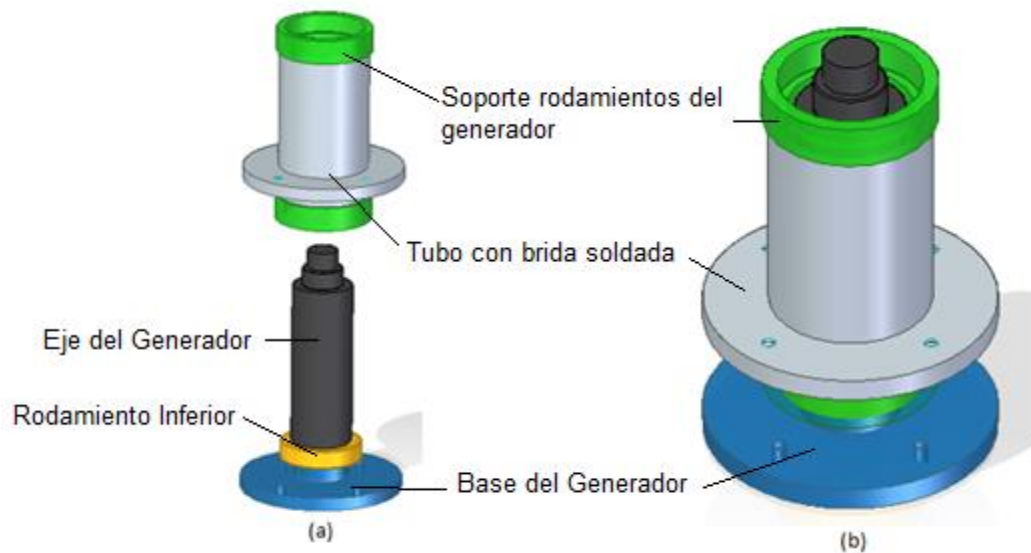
Acople del tubo con brida al sistema anterior ensamblado. (a) Forma de ensamble del tubo con brida y sus respectivos soportes soldados a este. (b) Visualización una vez ensamblado en el soporte y encajada la pista exterior del rodamiento.
